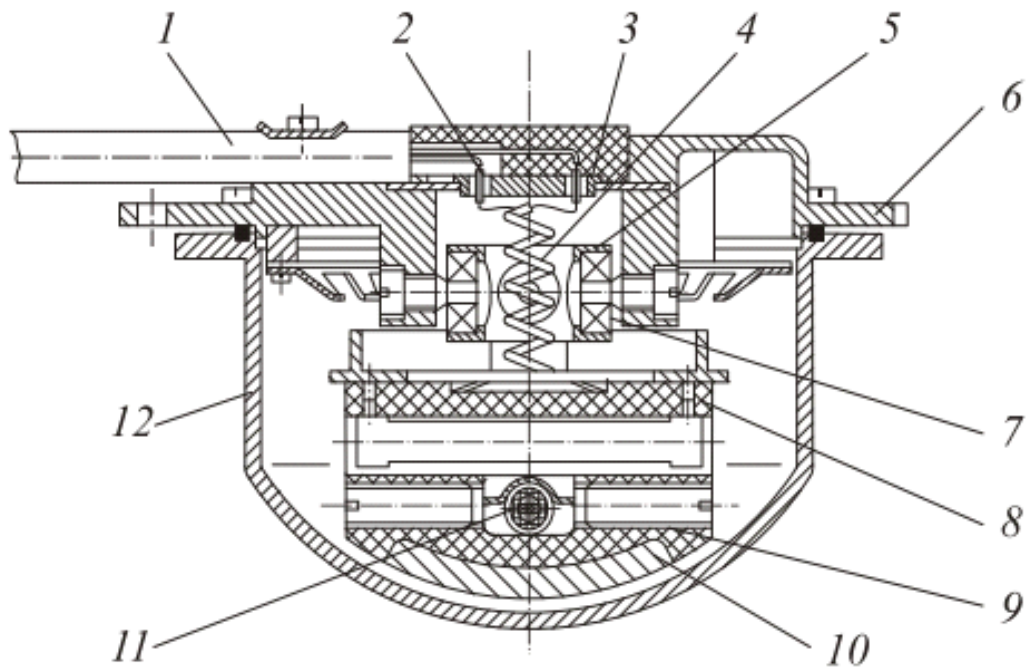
Конструкція серійного індукційного датчика ІД-6
